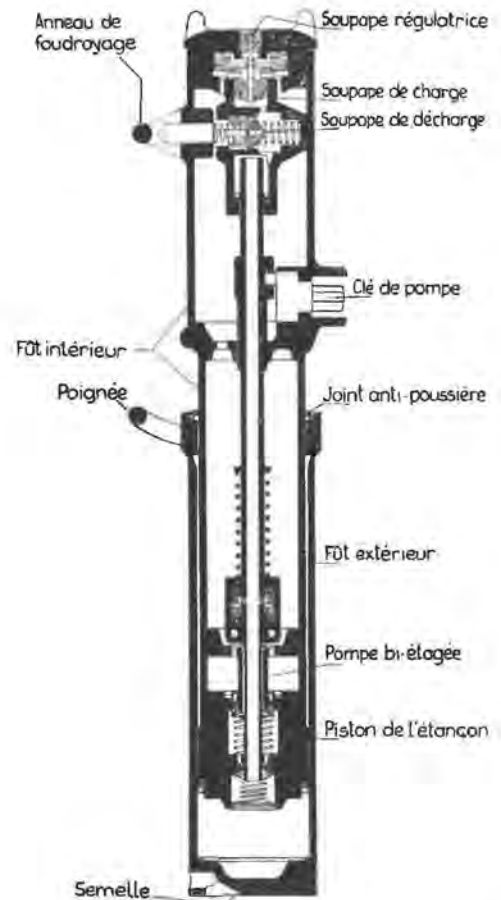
Coupe de l'étauçon hydraulique Eisenwerk-Wanheim.
